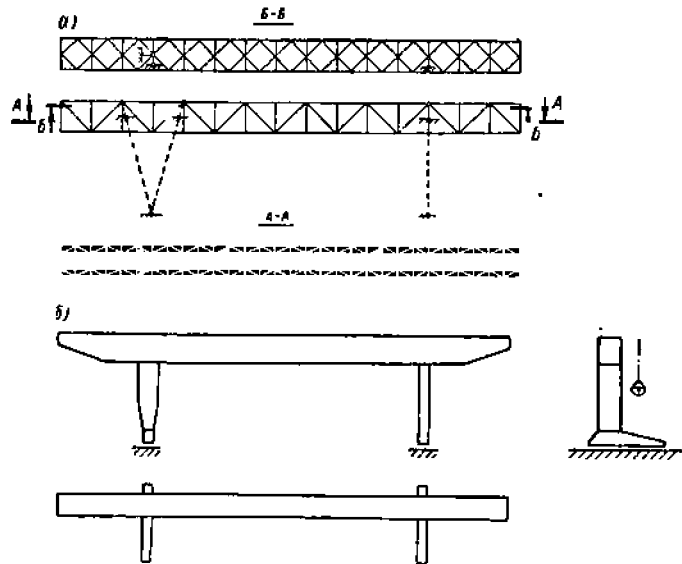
Типы металлических конструкций мостовых перегружателей: а — пролетное строение решетчатое, поперечные рамы см. рис. 3.57, и—о, конструкции опор см. рис. 3.58; б — пролетное строение однобалочное (см. рис. 3.43, з—м)
